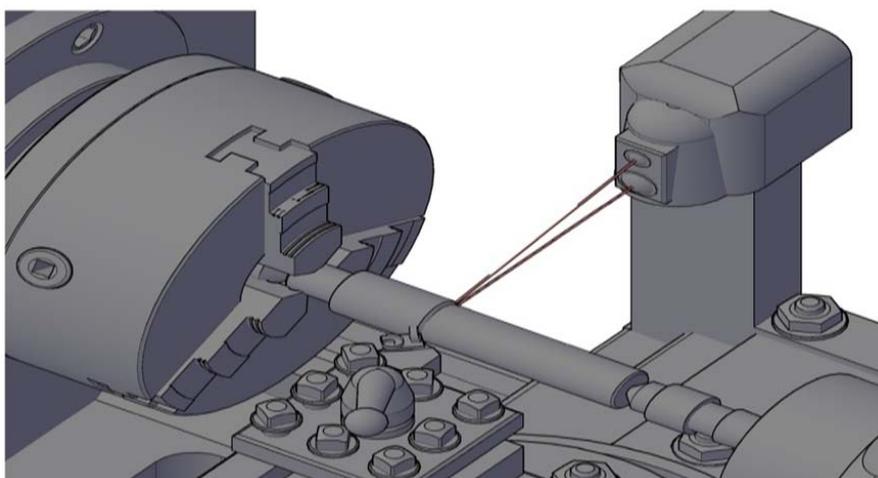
Обработка направляющей колонки с активным лазерным контролем
